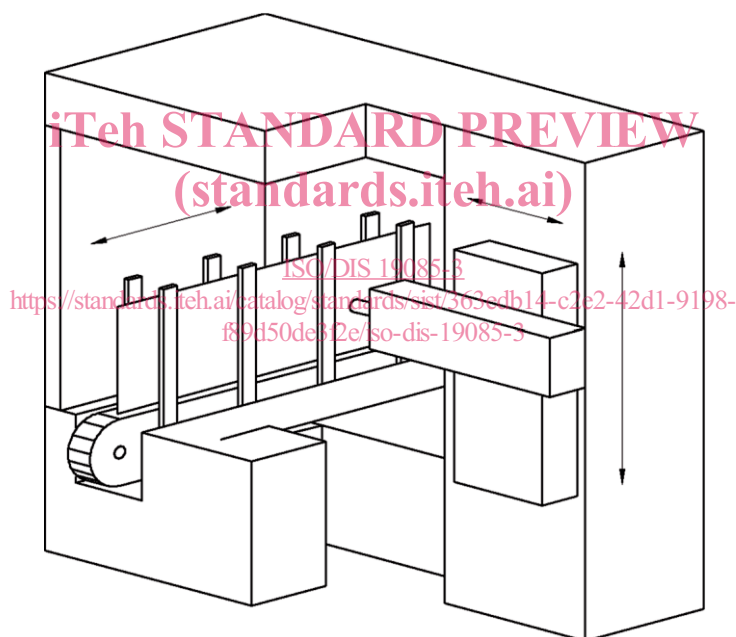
Exemple de machine verticale en enfilade avec pièce mobile, bâti fixe, tête d'usinage mobile
